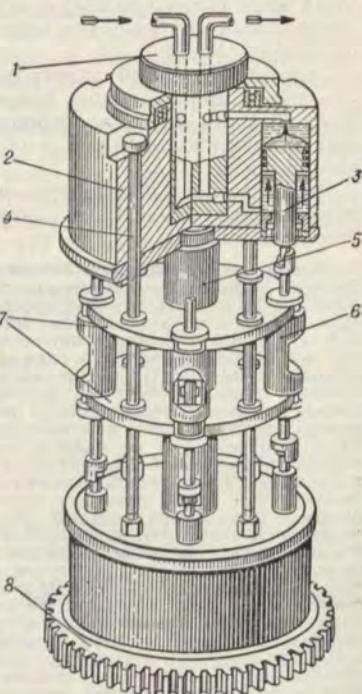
Схема двухстороннего гидравлического ротора: 1 — неподвижная пробка; 2 — блок цилиндра; 3 — поршень; 4 — стяжка рабочего ротора; 5 — вал ротора; 6 — блок инструмента; 7 — блокодержатель; 8 — приводная шестерня.
